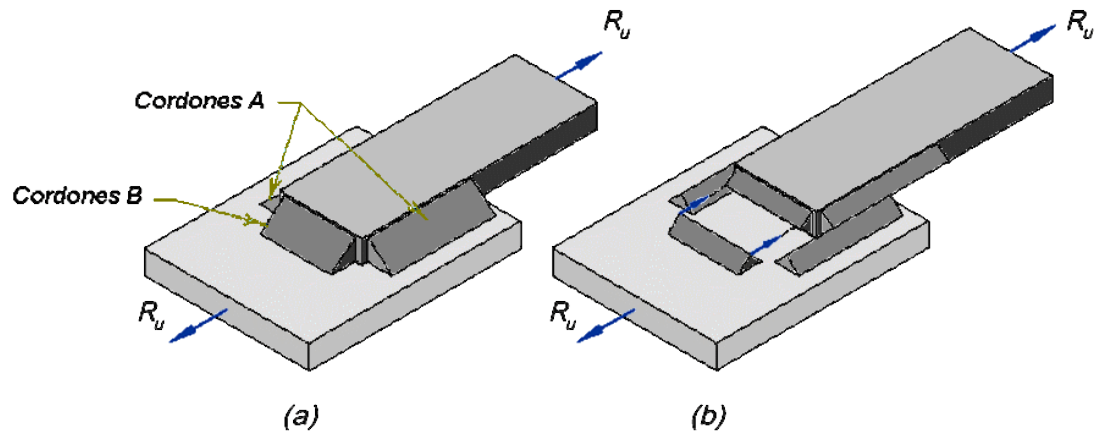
Soldadura a filete. Nota. Datos tomados de <http://webdelprofesor.ula.ve/nucleotrujillo/americanab/07-conexionessoldadas/7-11.html>
